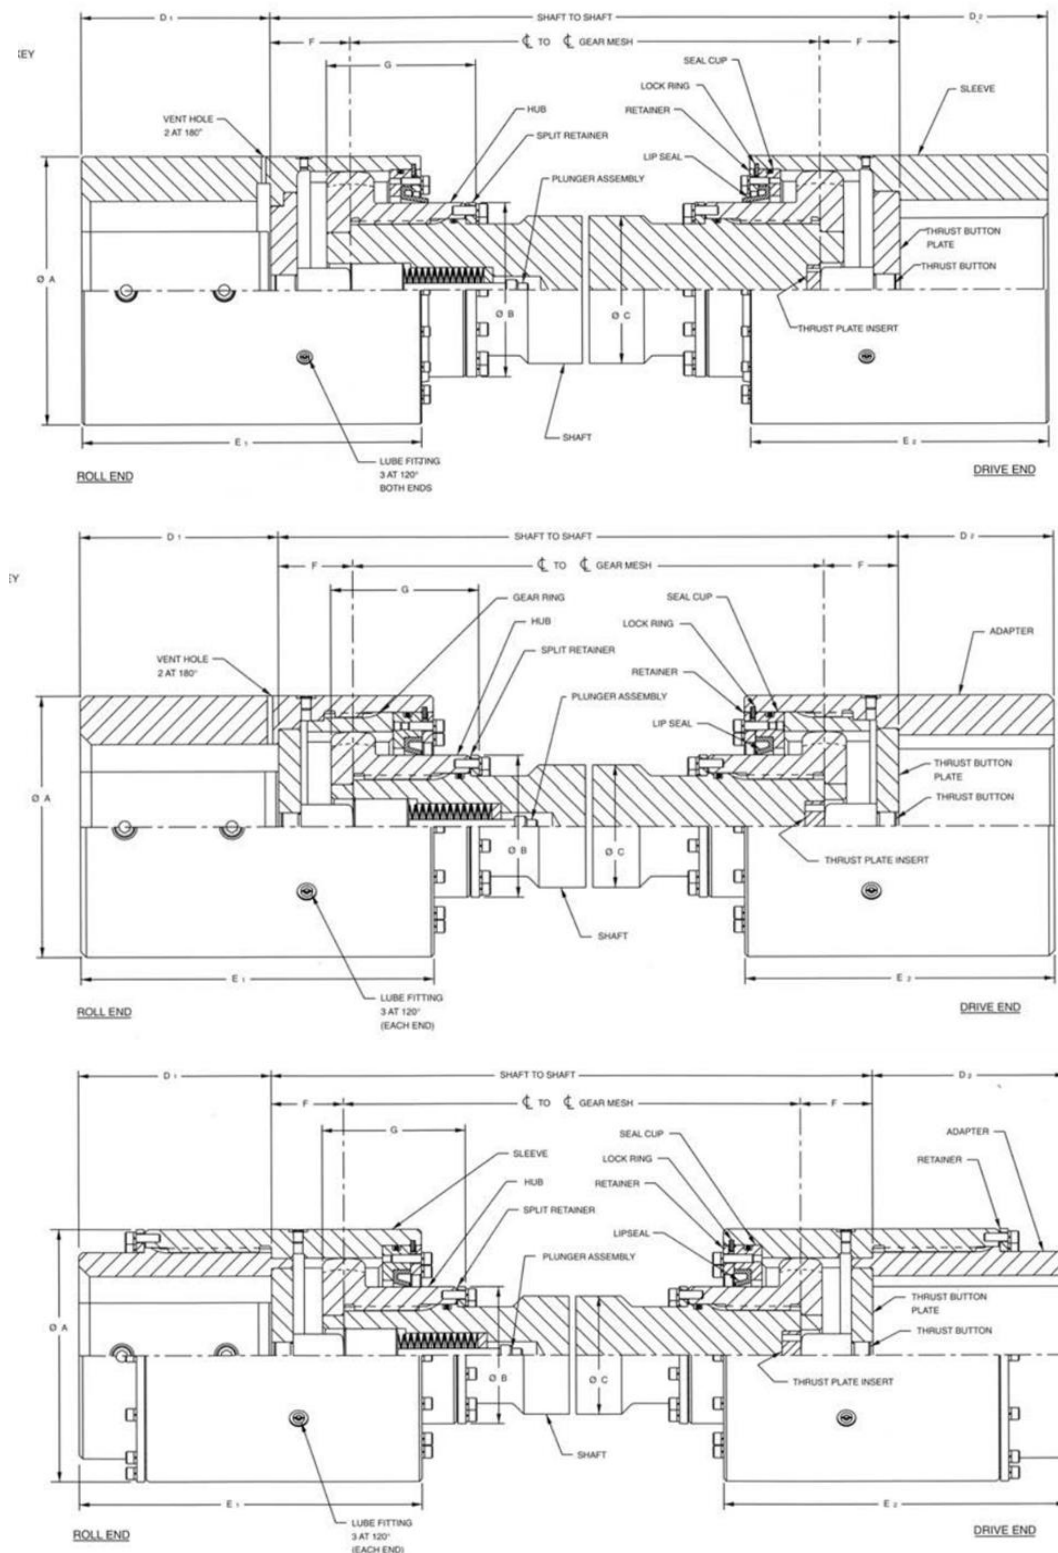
Основні типи конструкцій шпинделів з зубчастими шарнірами
